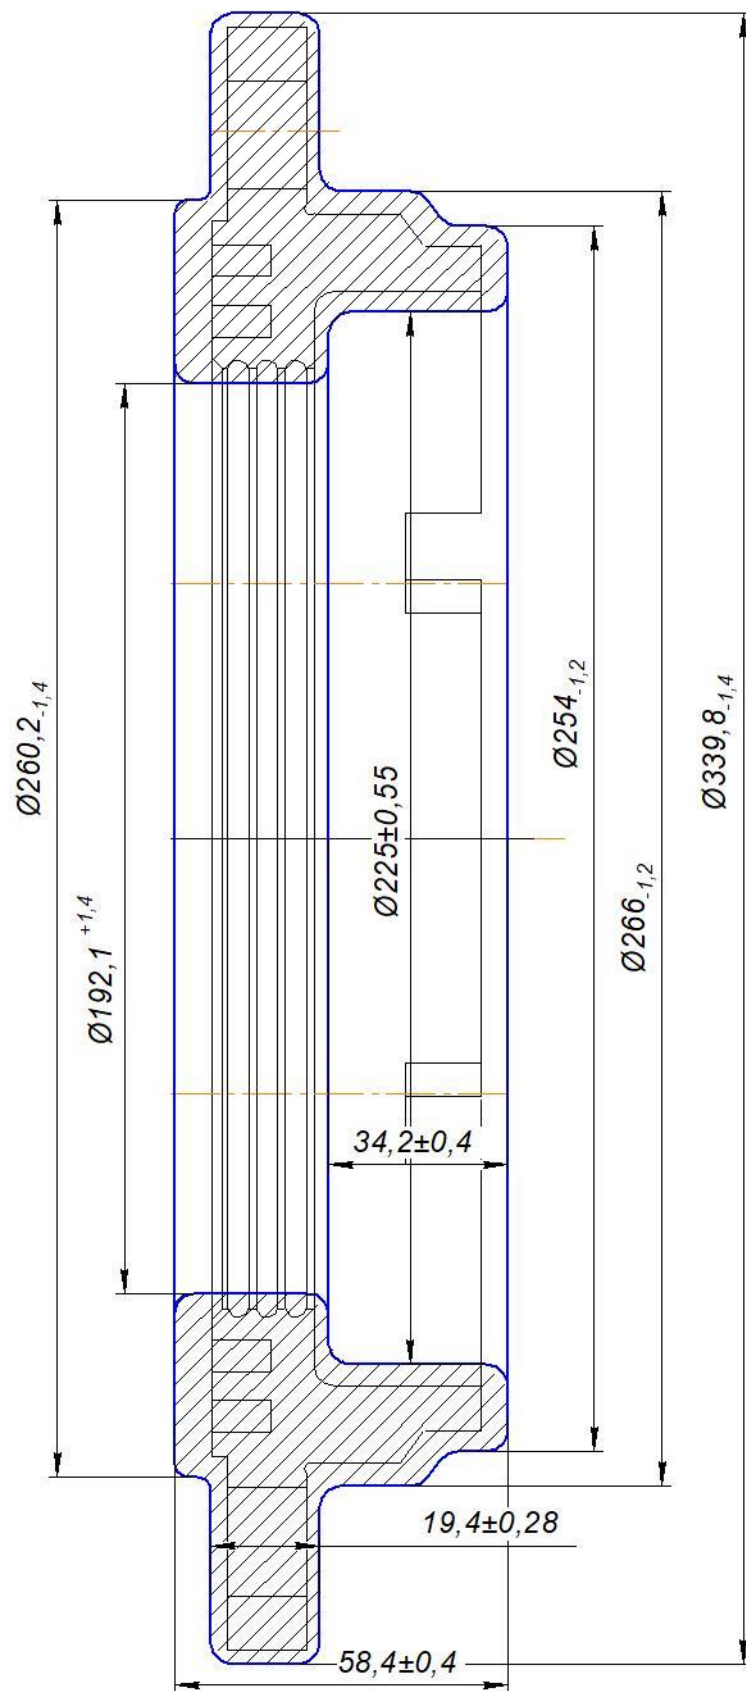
Ескіз заготовки кришки лабіринтної
